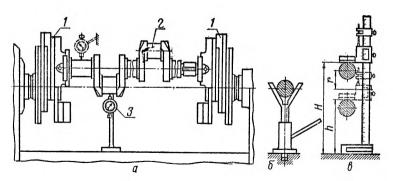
Схема установки коленчатого вала на станке для обработки шатунных шеек:
